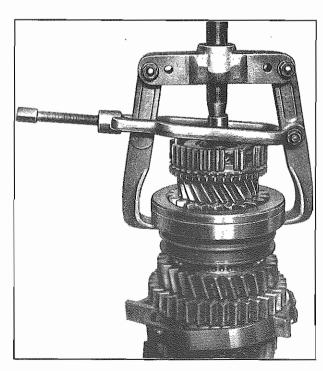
Ingranaggio della 3a marcia 3rd gear
